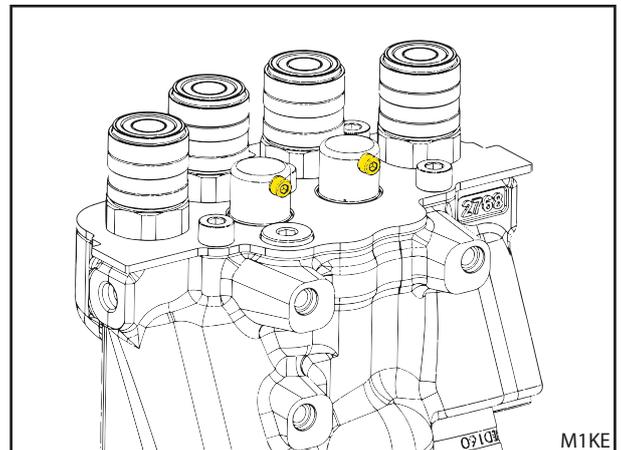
Position der Hydraulikschrauben bei einem Hydac-Ventil
